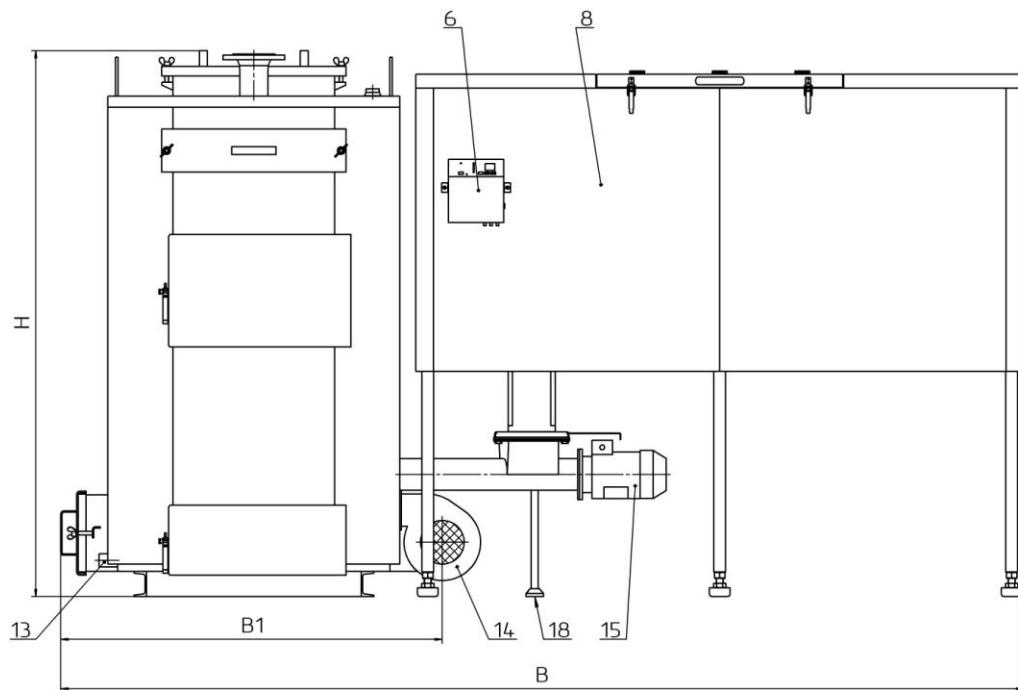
Внешний вид и основные элементы котла типа КТ-3Е-SН
